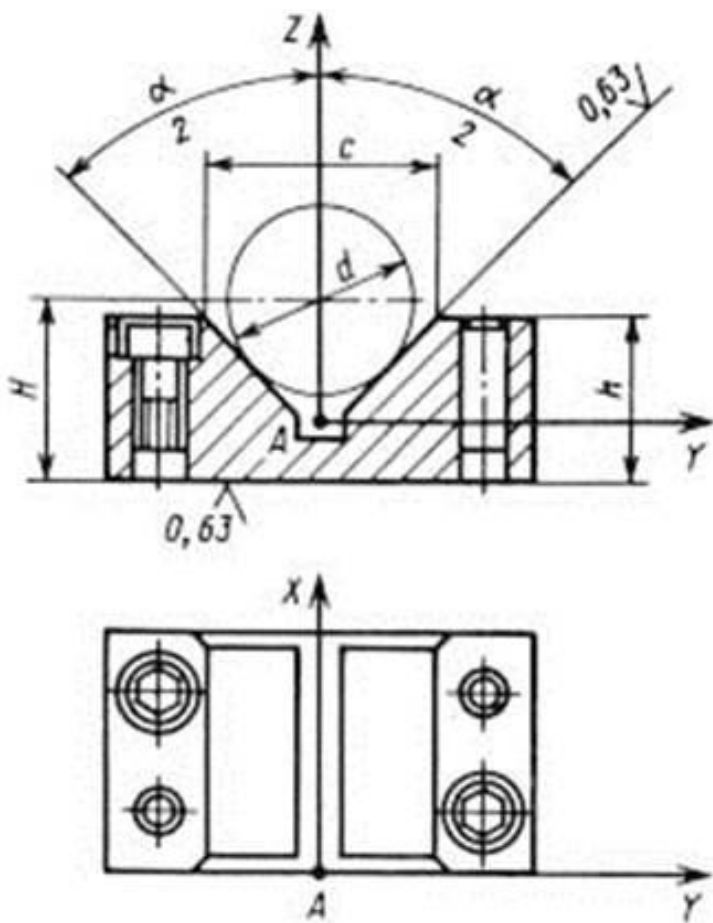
Призма ГОСТ 12195 – 68 для установки цилиндрических заготовок по «чистым» (обработанным) поверхностям.
